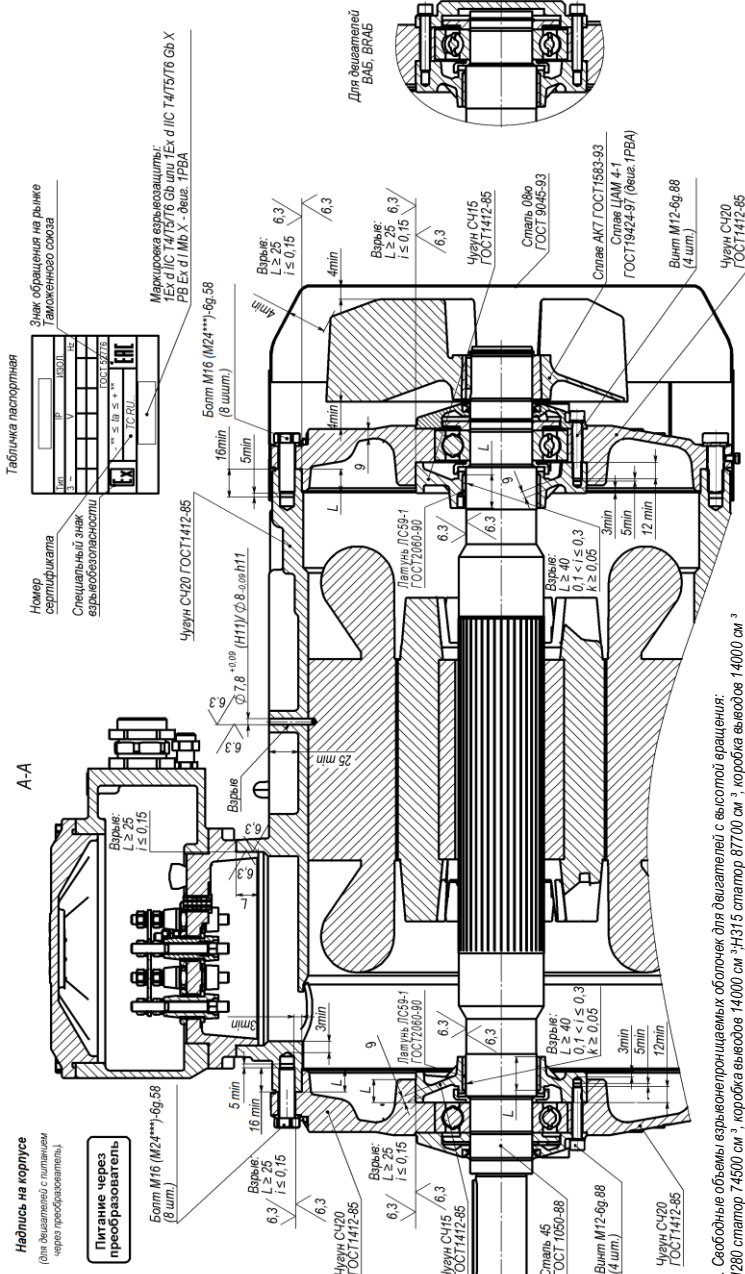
Чертеж взрывозащиты коробки выводов «д»
